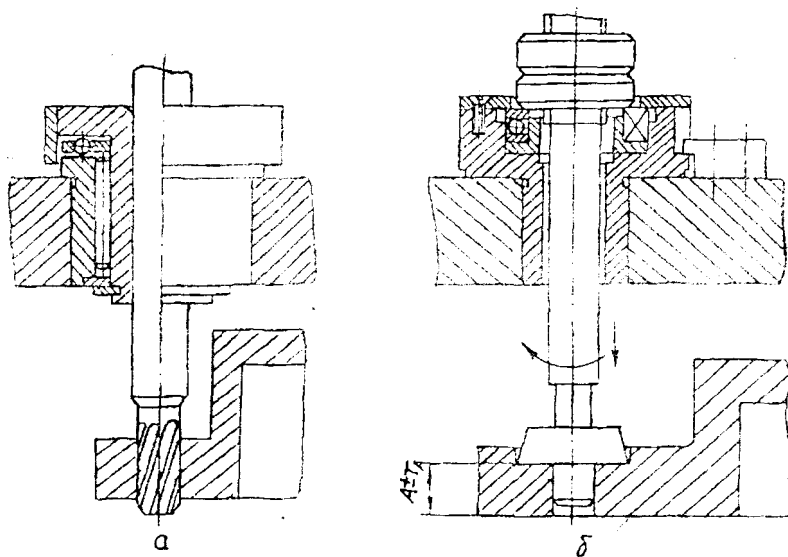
Вращающиеся втулки: а – для направления инструмента (развертки); б – кондукторная упорная
